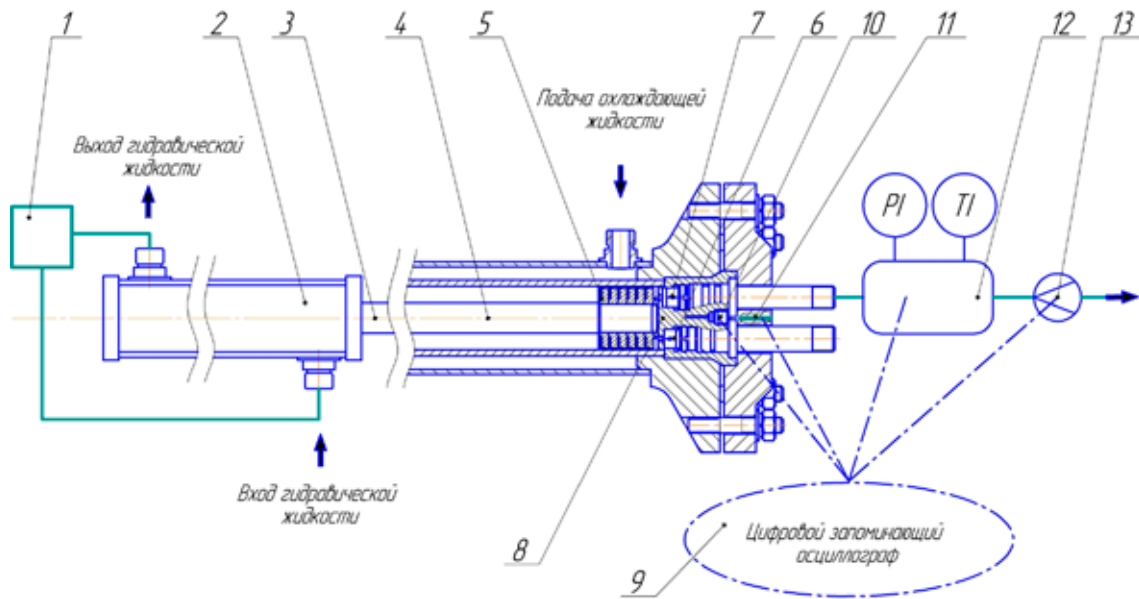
Схема тихоходной длинноходовой ступени поршневого компрессора с линейным гидроприводом:
